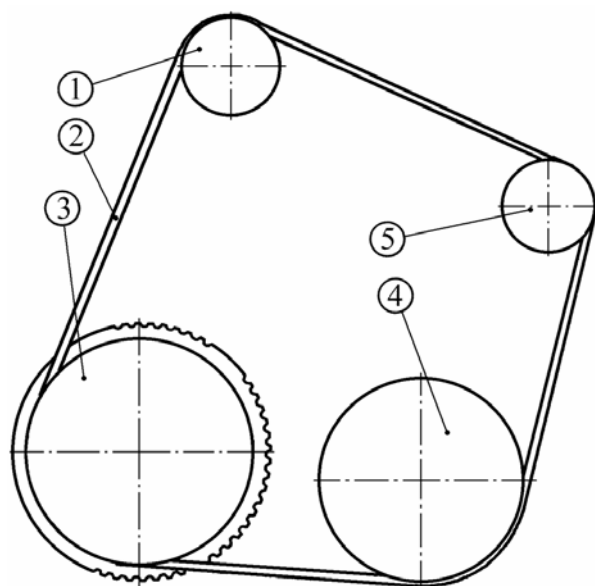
Схема установки ремня привода вспомогательных агрегатов:
